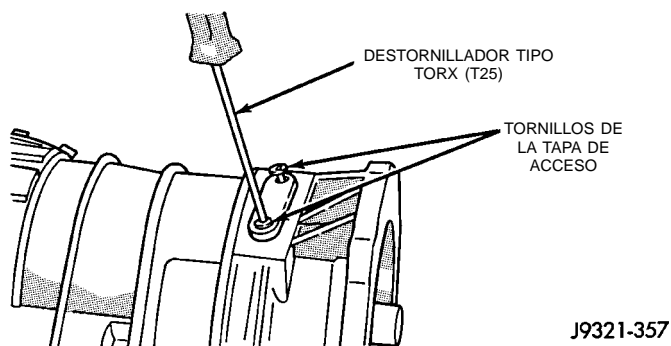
Desmontaje/instalación del tornillo de la tapa de acceso
